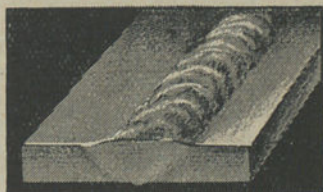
Corte duma soldadura depois de ensaio de corrosão, mostrando a boa penetração.
